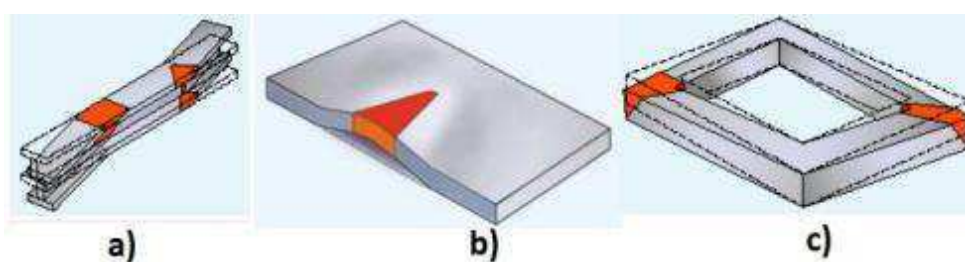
Exemplo de aplicação, a) perfil laminados, b) chapa, c) estrutura plana. (TWI,2014)
